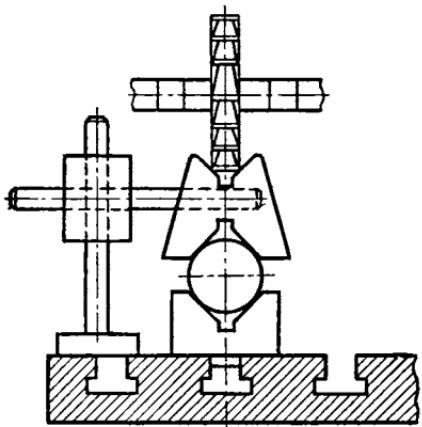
Приспособление для установки дисковой фрезы при фрезеровании паза на валу.
